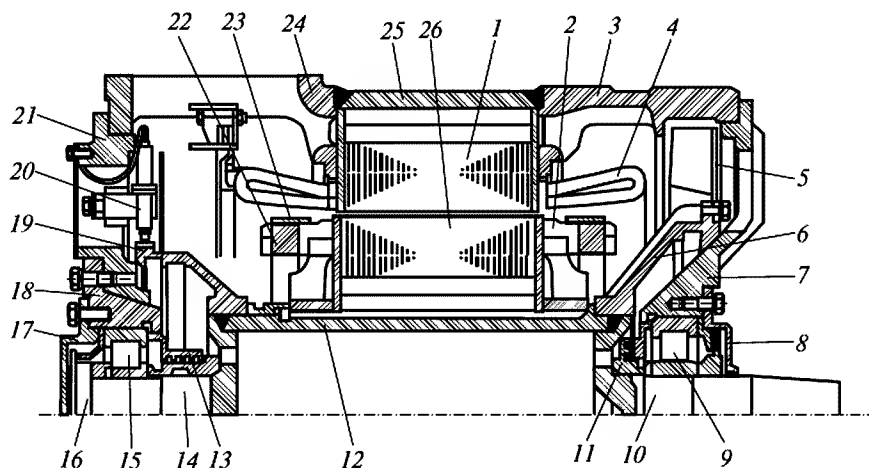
Продольный разрез асинхронного тягового двигателя НТА-350: 1 — сердечник статора; 2 — стержень ротора; 3, 24 — литые боковины; 4 — обмотка статора; 5 — вентиляционный диск; 6 — ступица вентилятора; 7, 21 — подшипниковые щиты; 8 — крышка подшипника; 9, 15 — подшипники; 10, 14 — цапфы; 11, 13 — лабиринтные уплотнения; 12 — барабан; 16 — упорная шайба; 17 — крышка подшипника; 18 — ступичная часть подшипникового щита; 19 — зубчатое колесо; 20 — считывающий элемент; 22 — короткозамкнутое кольцо; 23 — бандажное кольцо; 25 — стальная накладка; 26 — сердечник ротора
